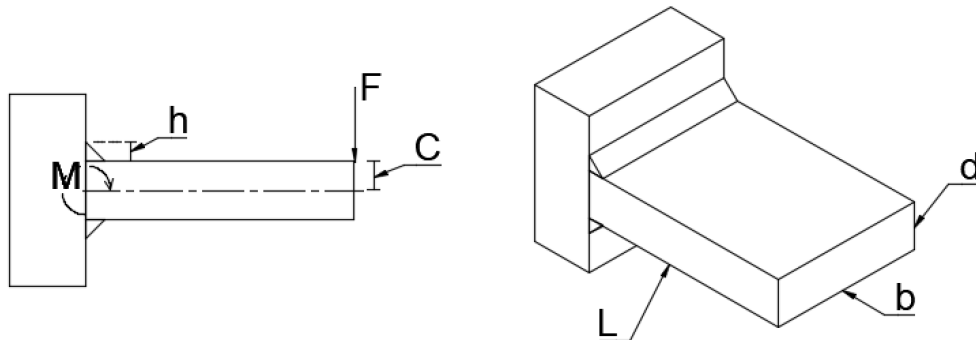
Dimensiones a considerar en el cálculo de soldadura
